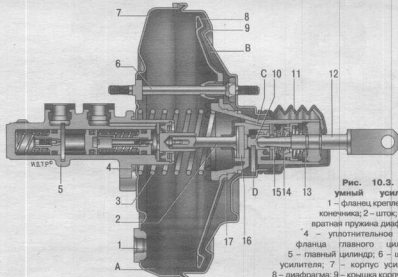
Вакуумный усилитель: 1 – фланец крепления наконечника; 2 – шток; 3 – возвратная пружина диафрагмы; 4 – уплотнительное кольцо фланца главного цилиндра; 5 – главный цилиндр; 6 – шпилька усилителя; 7 – корпус усилителя; 8 – диафрагма; 9 – крышка корпуса усилителя; 10 – поршень; 11 – защитный чехол корпуса клапана; 12 – толкатель; 13 – возвратная пружина толкателя; 14 – пружина клапана; 15 – клапан; 16 – буфер штока; 17 – корпус клапана; А – вакуумная камера; В – атмосферная камера; С, D – каналы
